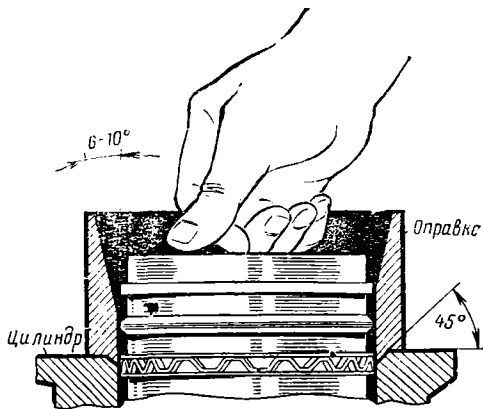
Оправка для установки поршня со стальными кольцами в цилиндр
